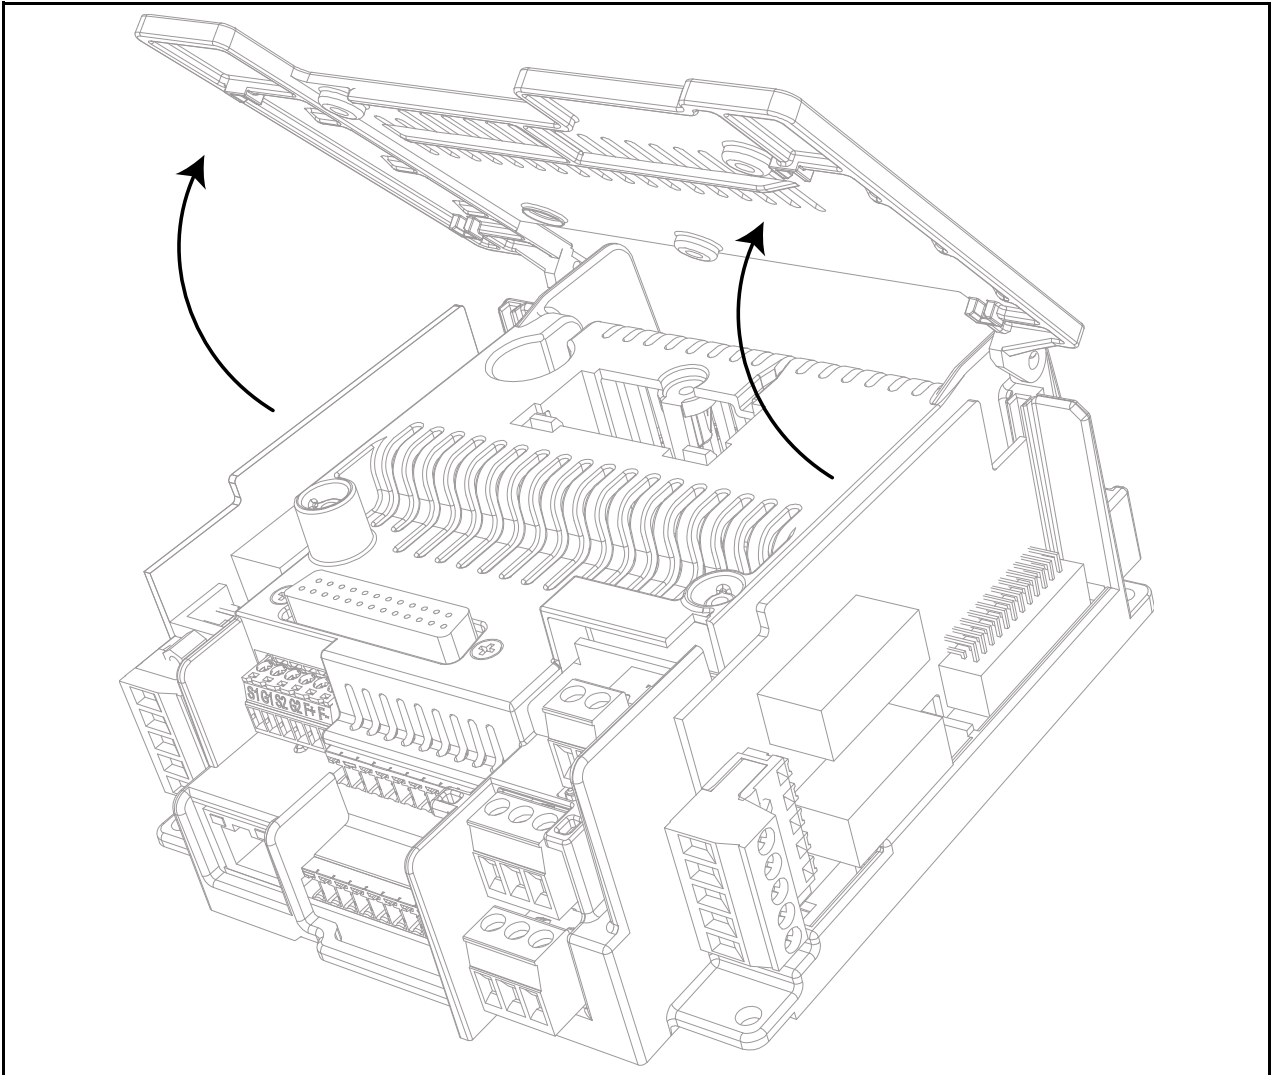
Öffnen Sie die Abdeckung des Steuerkastens.
